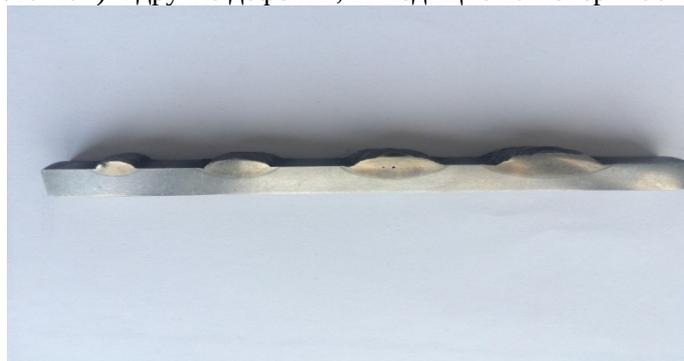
Газовые поры, выявленные на макрошлифе сварного шва
